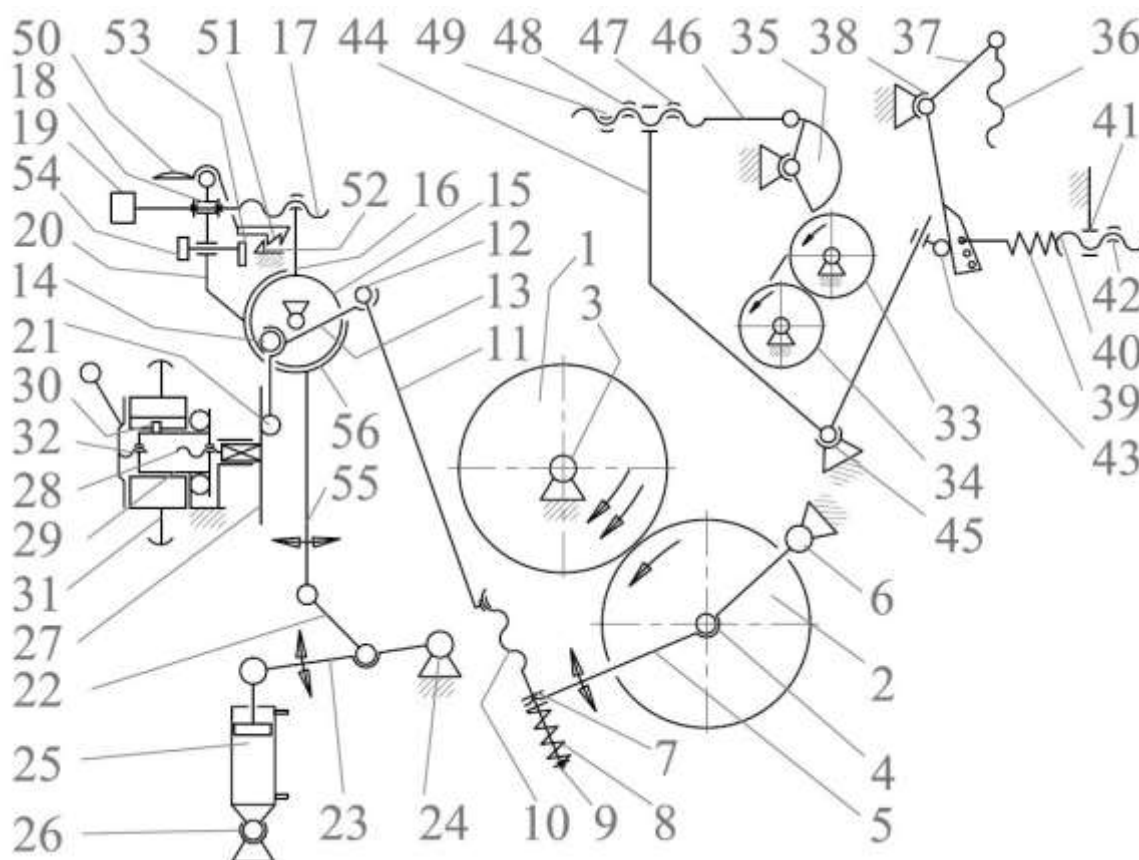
Кінематична схема вальцевого верстата А1-БЗН.
